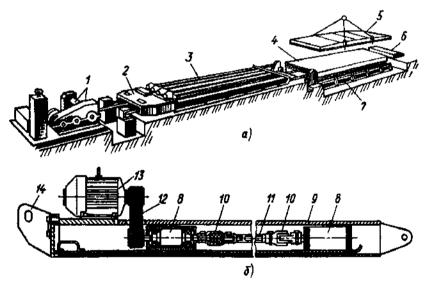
Формовочная машина: а – общий вид; б – пустотообразователь
